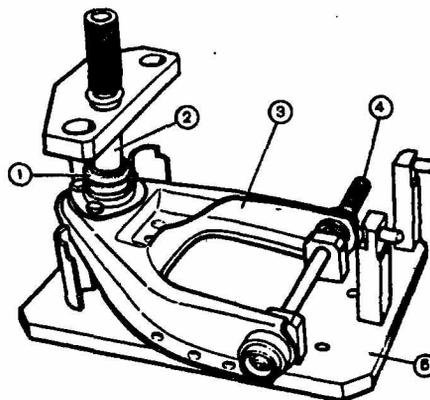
Проверка левого верхнего рычага: 1 - палец для центровки шарниров; 2 - верхний рычаг; 3 - оправка для центровки шарового шарнира; 4 - шаровой шарнир; 5 - приспособление А.95716
